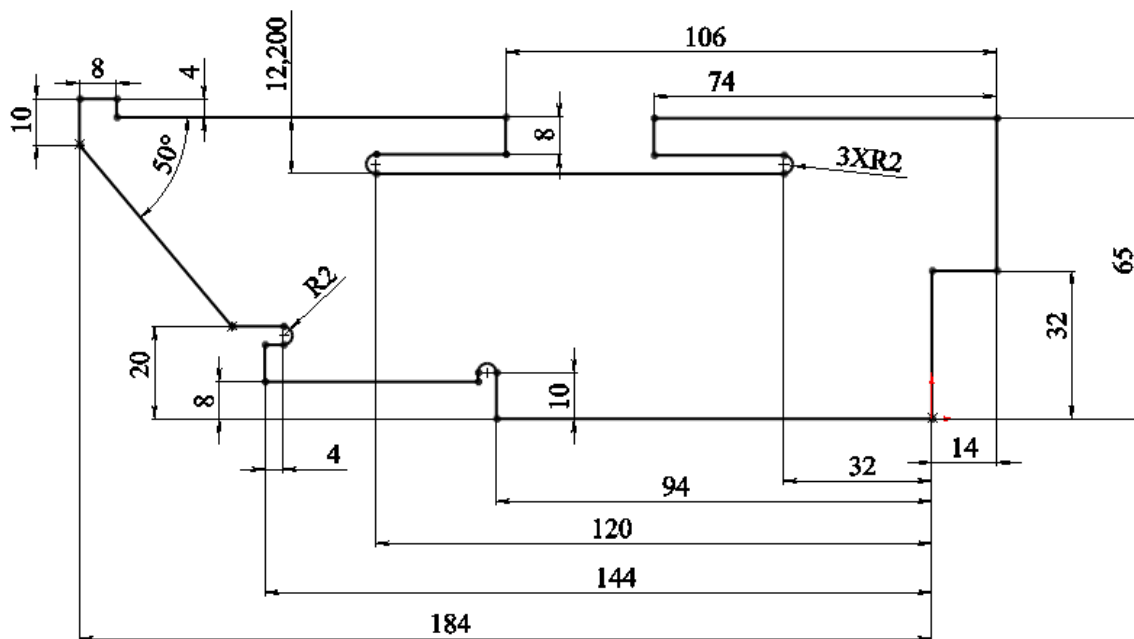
Эскиз для Базовой кромки детали «Стенка внутренняя»
